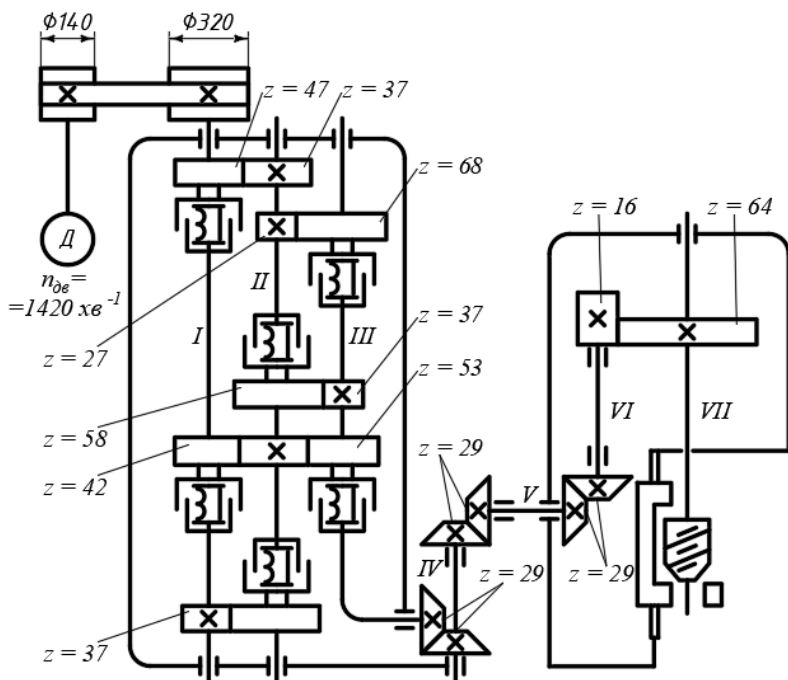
Кінематична схема коробки швидкостей зубофрезерного верстата (приклад)
